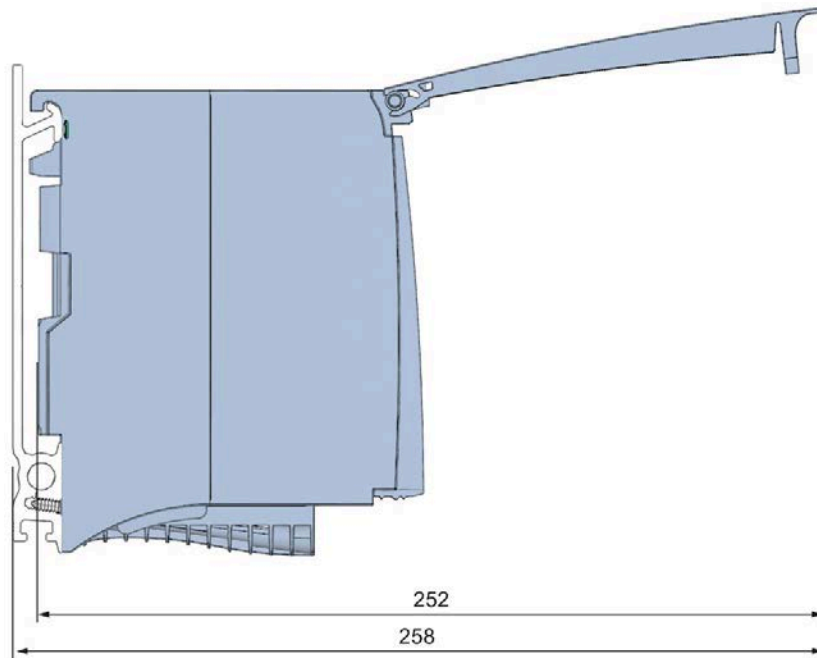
Maßbild des Moduls PS 25W 24VDC in Seitenansicht mit geöffneter Frontklappe
